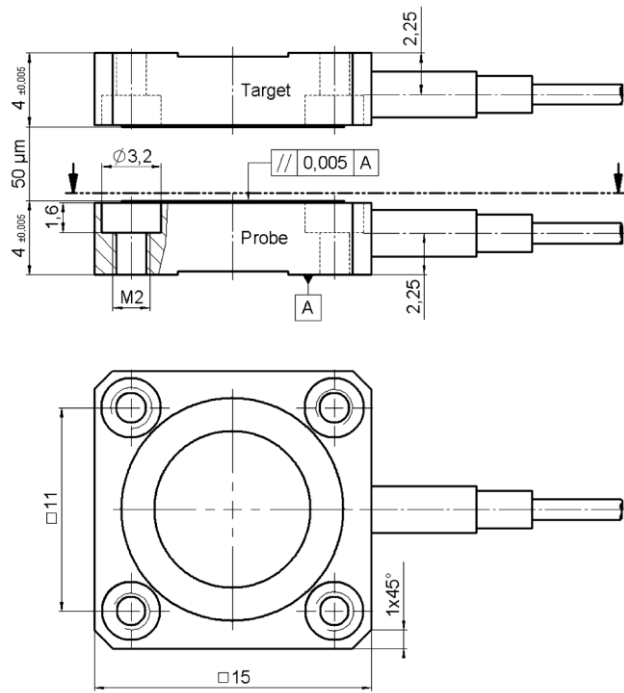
Габаритный чертёж датчика D-050.00. Размеры указаны в мм.
